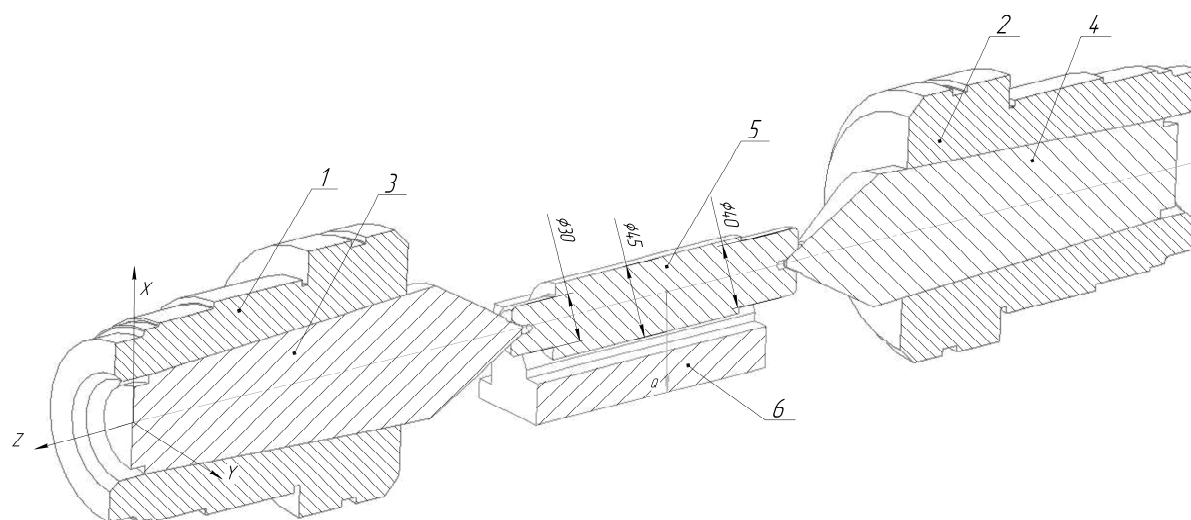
Конструкція двохповодкового двобічного фрикційного приводу деталі:
